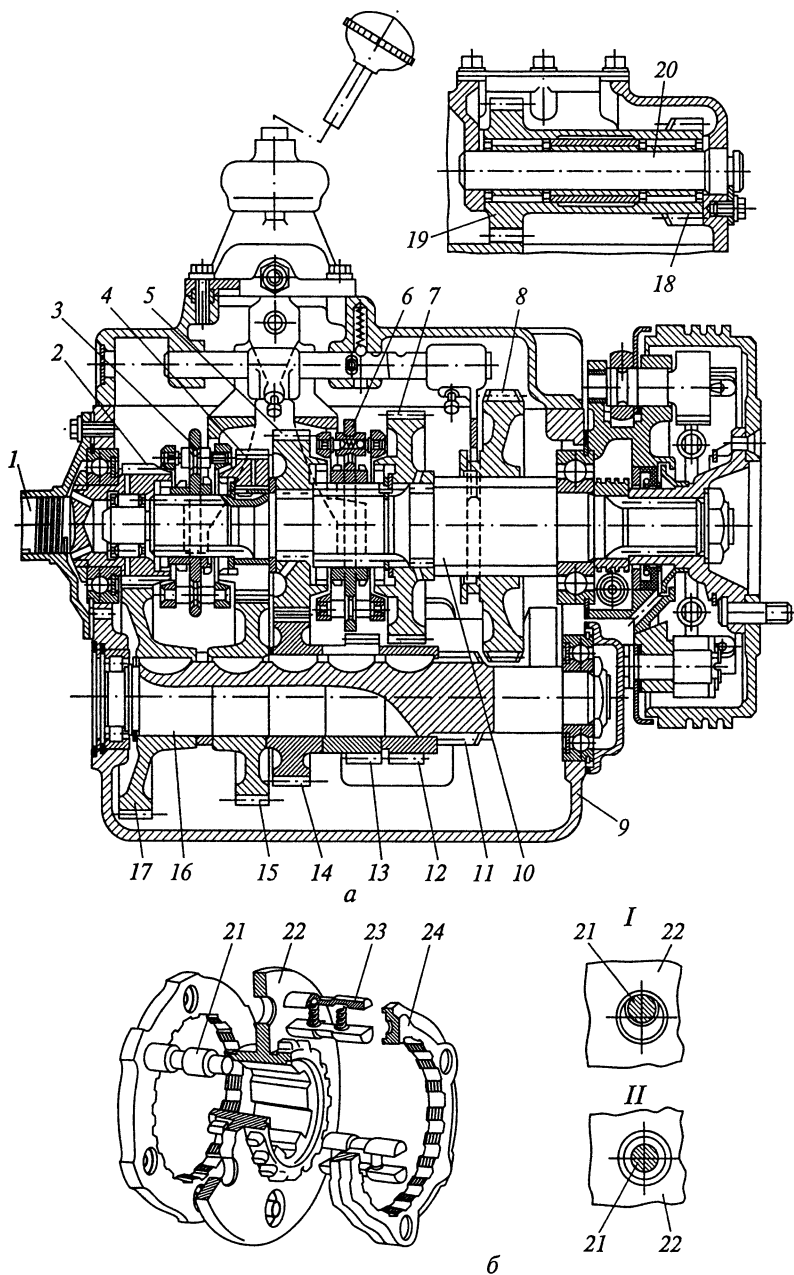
Коробка передач грузовых автомобилей ЗИЛ:
